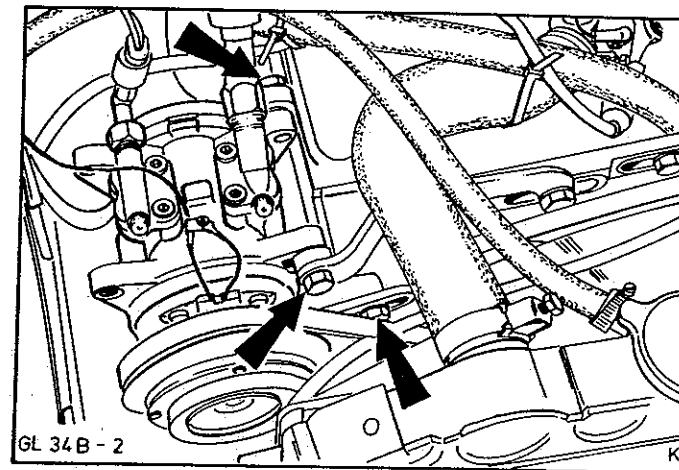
Befestigungsschrauben (3) am Kompressor lösen
